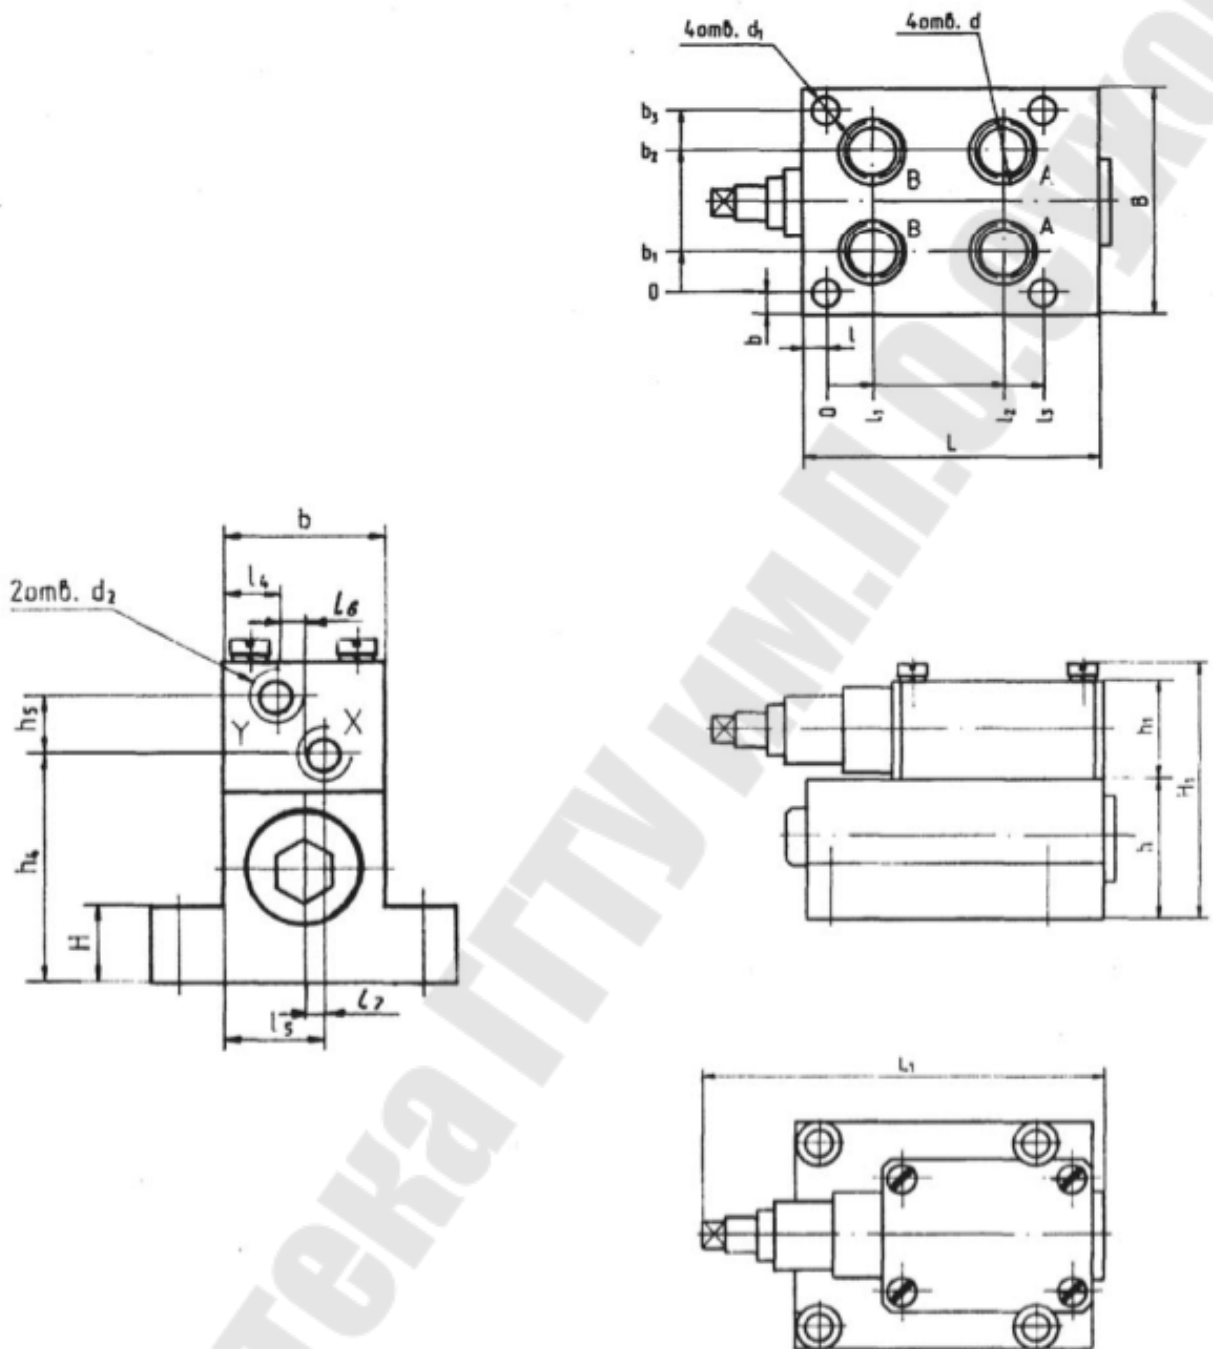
Общий вид блока присоединительного клапана редукционного БПВ-...КР, Ду=10, 16, 20, 32 мм
